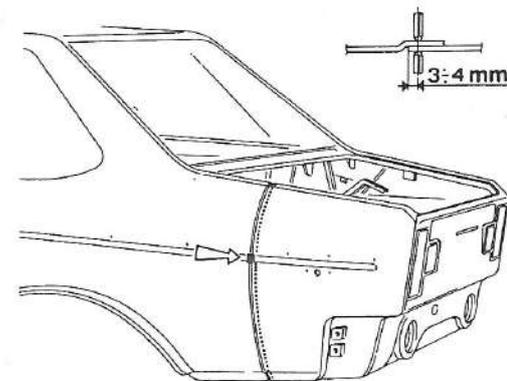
La siguiente operación consiste en la soldadura por puntos reservando la zona indicada por la flecha para la soldadura de atmósfera de gas inerte.
